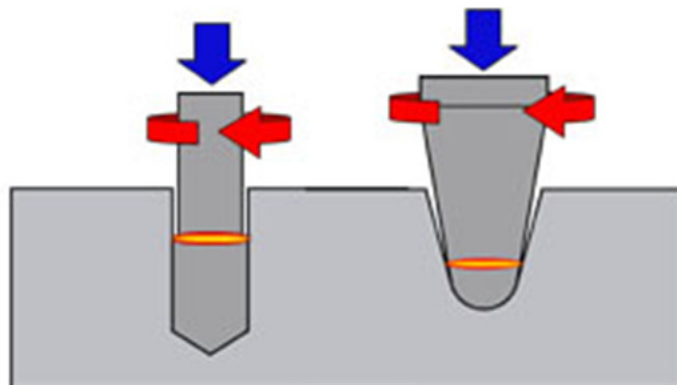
Geometrias de soldagem por fricção com pino consumível <sup>(37)</sup>.
